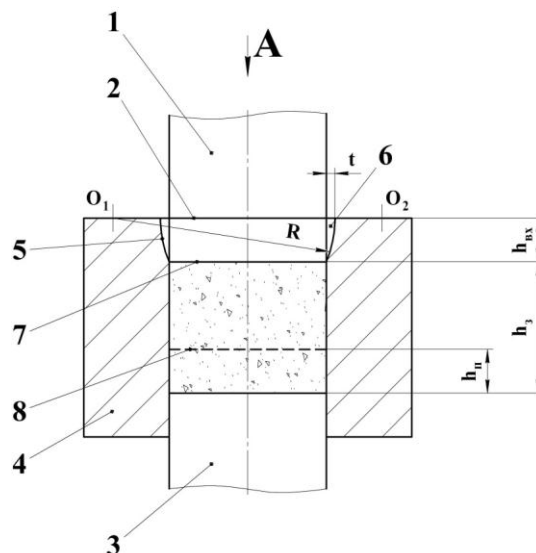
Схема пресс-формы для формования порошков: 1 – верхний пуансон с рабочей поверхностью 2; 3 – нижний пуансон; 4 – матрица со входным участком 5 и каналами 6; 7 – поверхность засыпки смеси; 8 – поверхность будущей прессовки
